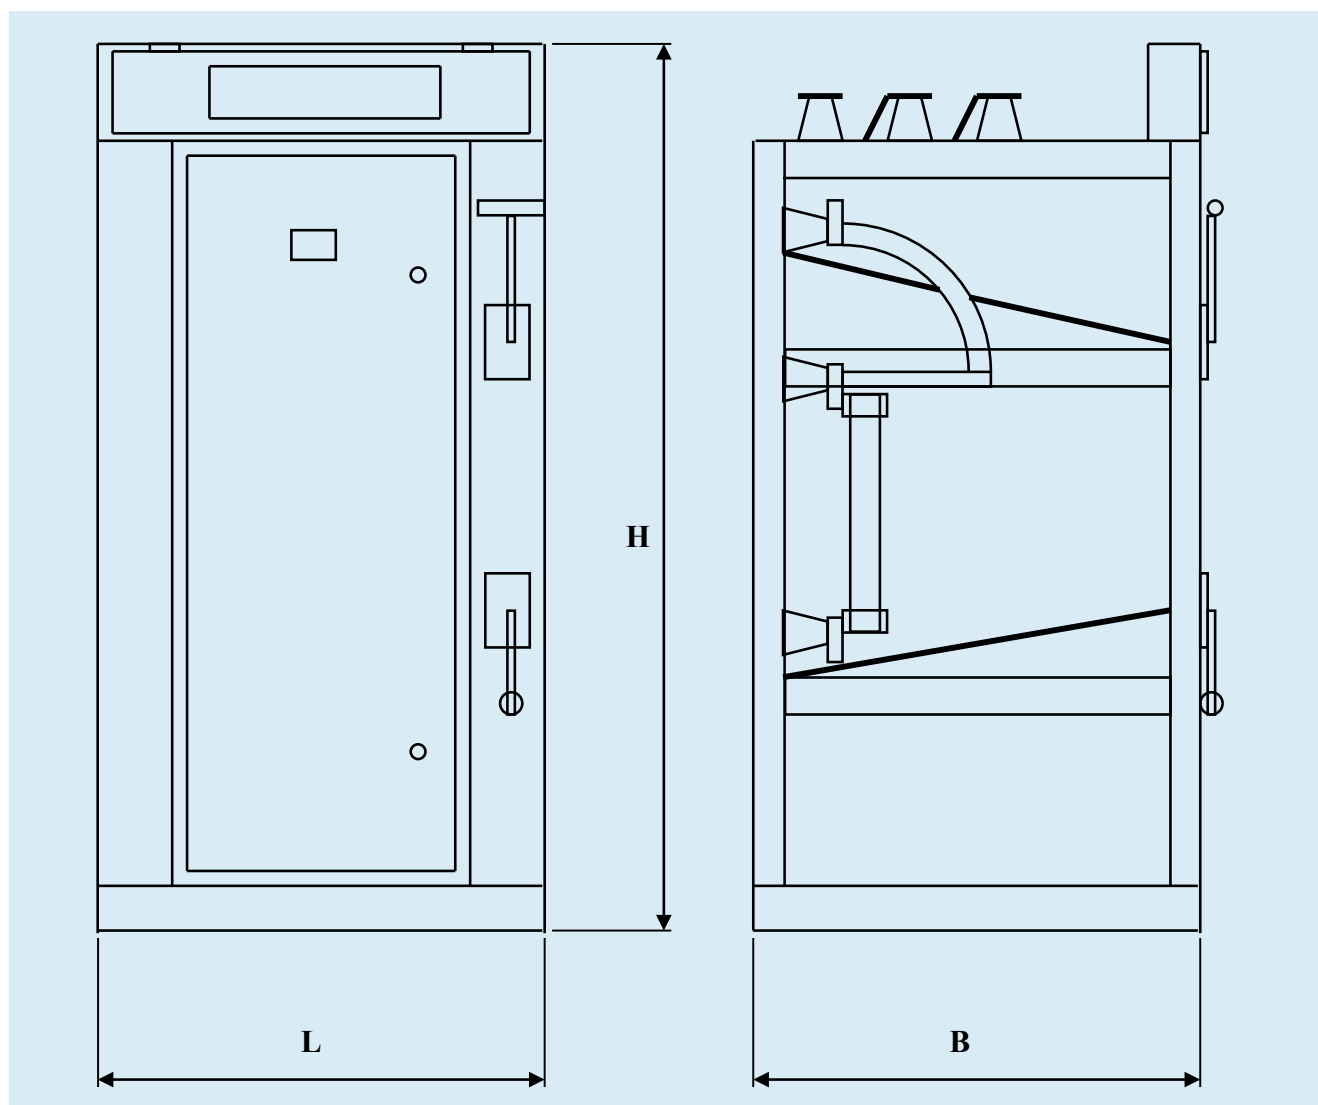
Общий вид и габаритные размеры камер КСО-366, КСО-394М
